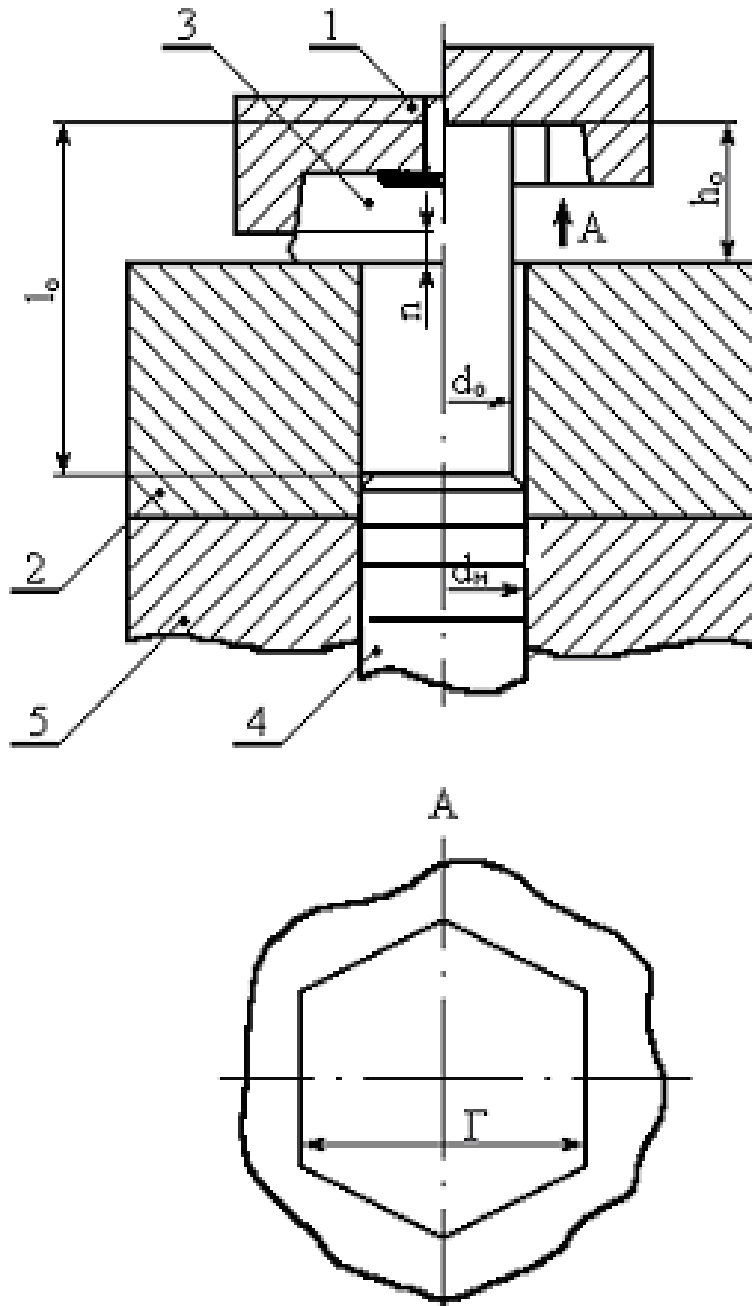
Загальний вид експериментального штампу: 1 – пуансон; 2 – матриця; 3 – корпус;
